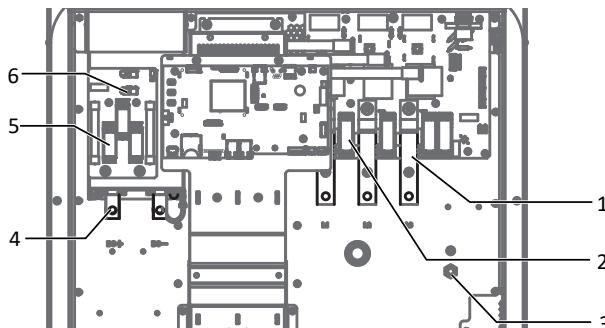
Área de conexión del lado de CC (izquierda) / lado de CA (derecha)
